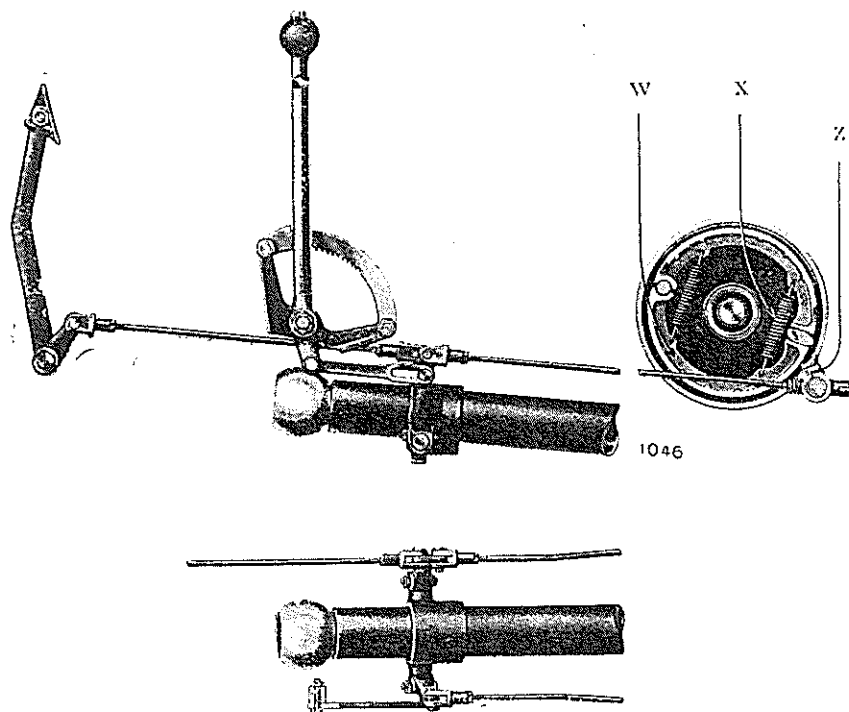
COMMANDE DU FREIN ARRIÈRE.
